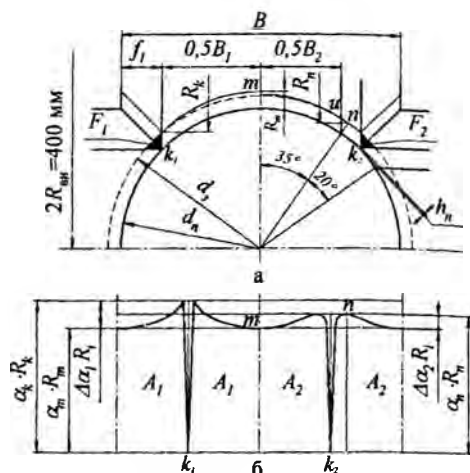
Схема калибров «круг-круг» (а) и поверхности контакта валков с заготовкой (б) в четырехвалковом калибре
